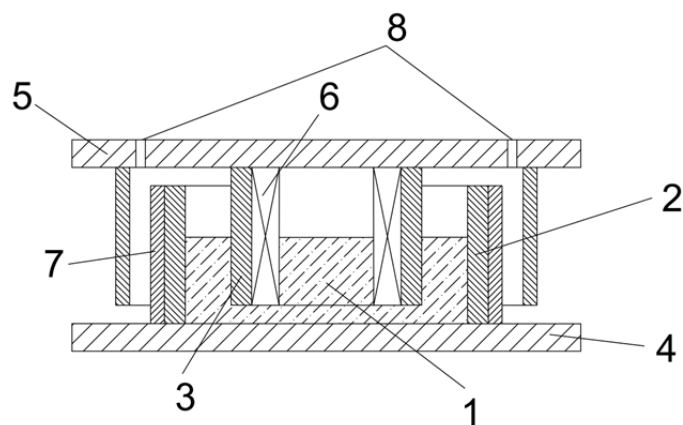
Реологическая опора: 1 – объем ферромагнитной жидкости; 2 – цилиндрический корпус; 3 – поршень; 4 – нижняя присоединительная плита; 5 – верхняя присоединительная плита; 6 – герметизированная тороидальная катушка индуктивности; 7 – полупроводниковый термоэлектрический элемент; 8 – вентиляционные отверстия
